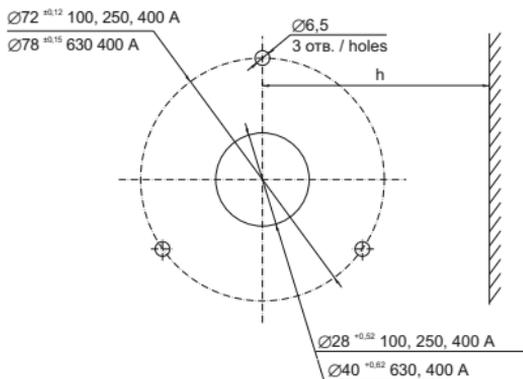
Отверстия в стенке шкафа для установки боковой смещенной рукоятки /
